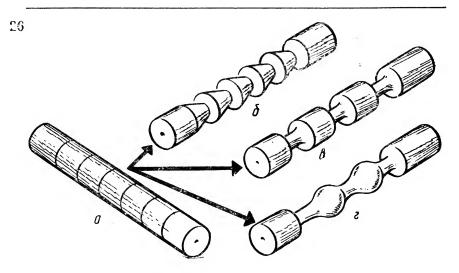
Валики для упражнений: а — заготовка валика; б — валик с острыми гребнями; в — валик с галтелями; г — валик с плавными переходами.
